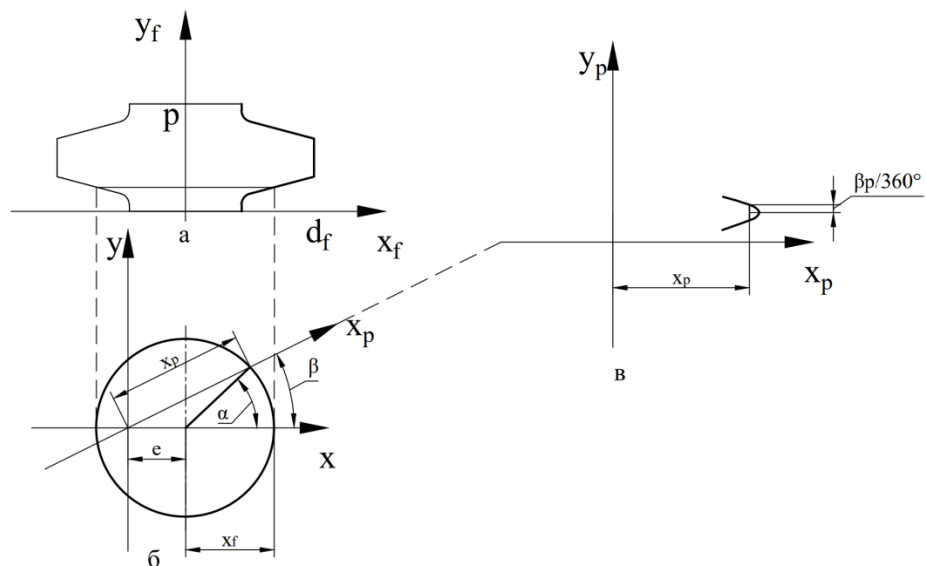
Схема получения профиля резьбы. а – профиль инструмента, б – сечение инструмента, в – профиль резьбы.
